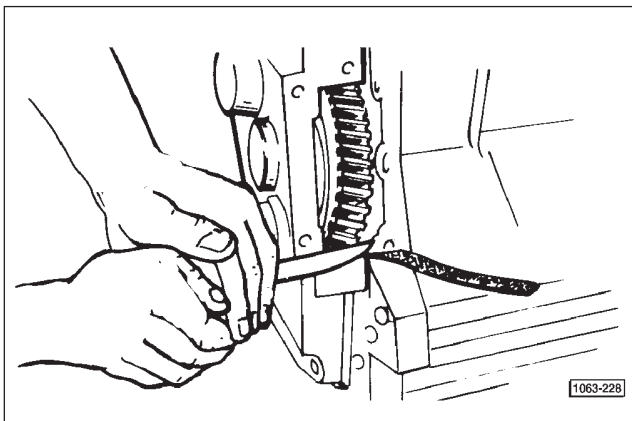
Découper la pièce excédente du joint à hauteur du plan de fixation prévu pour applications externes.
